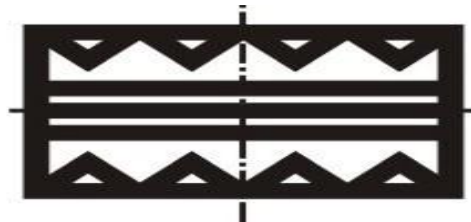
Прямоугольные отверстия в почвообрабатывающем катке: 1-прямоугольное отверстие, 2-зубчатые края, 3-резаки с лезвиями из нержавеющей стали.
